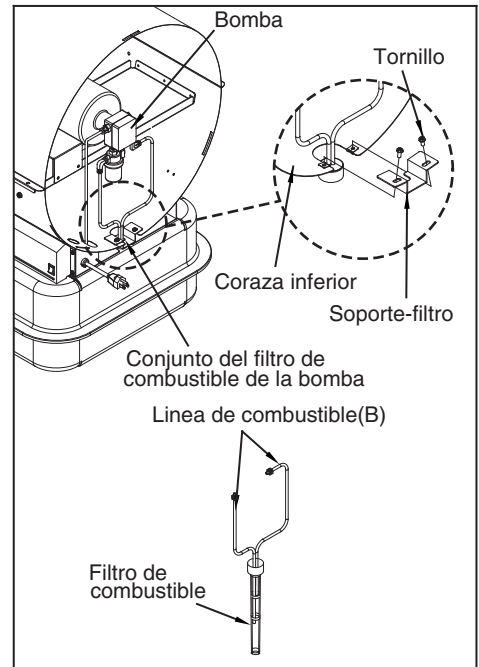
Desmontaje del Filtro de Combustible del Tanque
